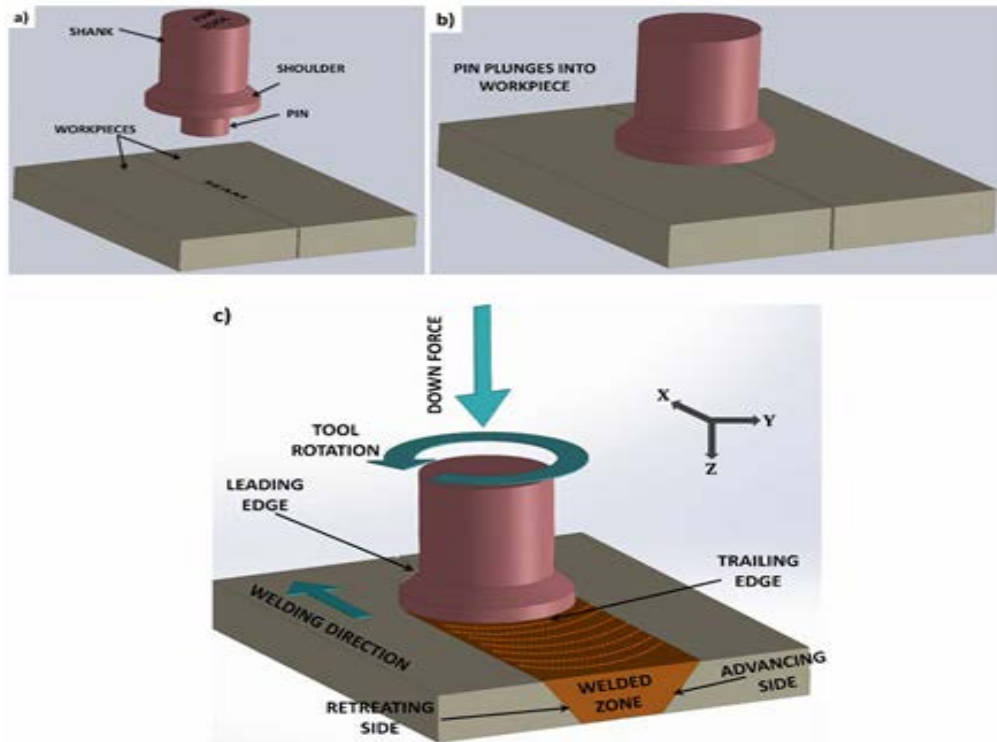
2 : Schéma de principe du soudage par points (FSW) : a) disposition des joints bout à bout ; b) outil entrant dans la pièce et c) nomenclature de soudage.
